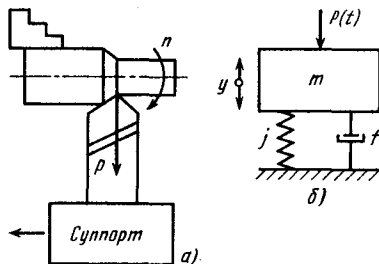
Суппорт токарного станка (а) и его одно-массовая динамическая модель (б)
